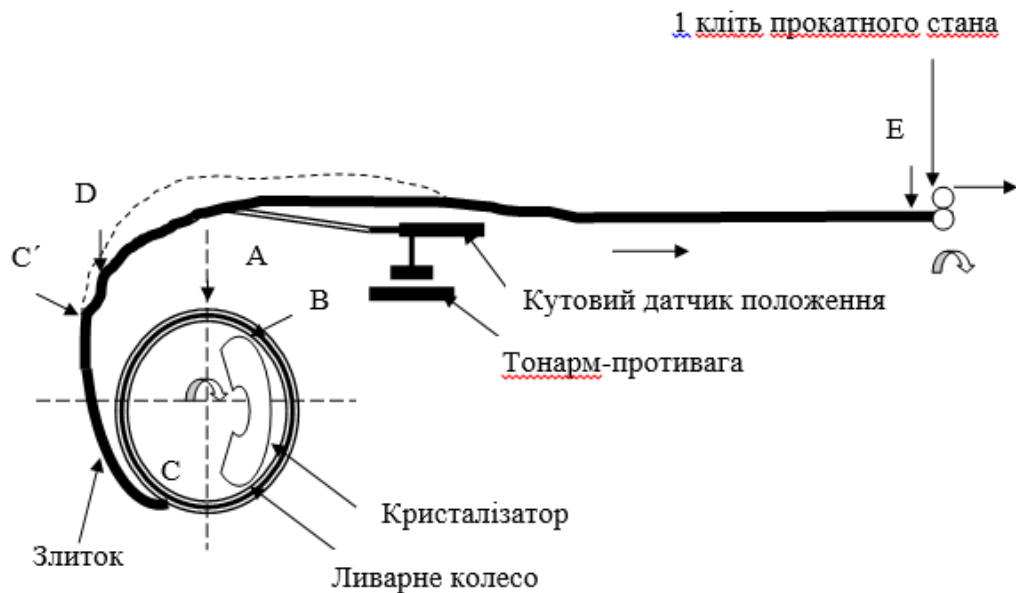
Схема формування алюмінієвої заготовки під час лиття
